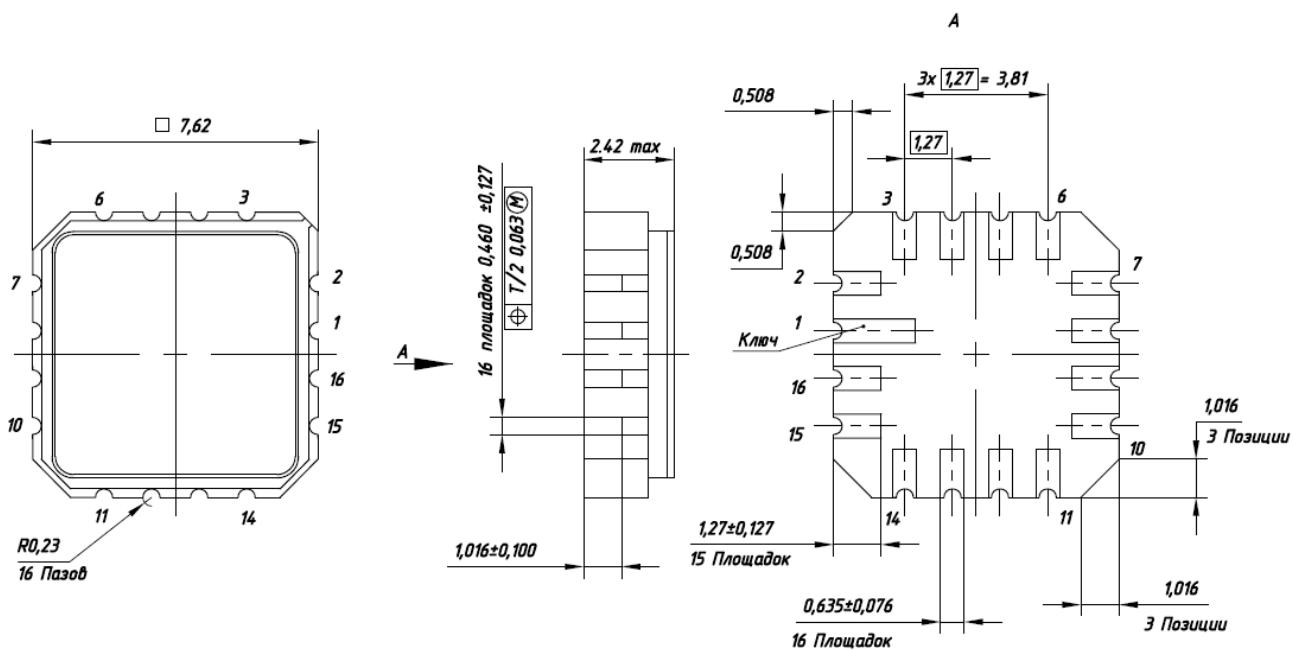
Габаритный чертеж корпуса Н04.16-1В
